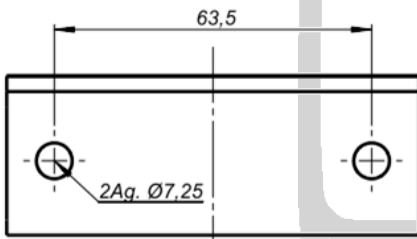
Dimensión e/c para tornillos de soporte a tablero.
